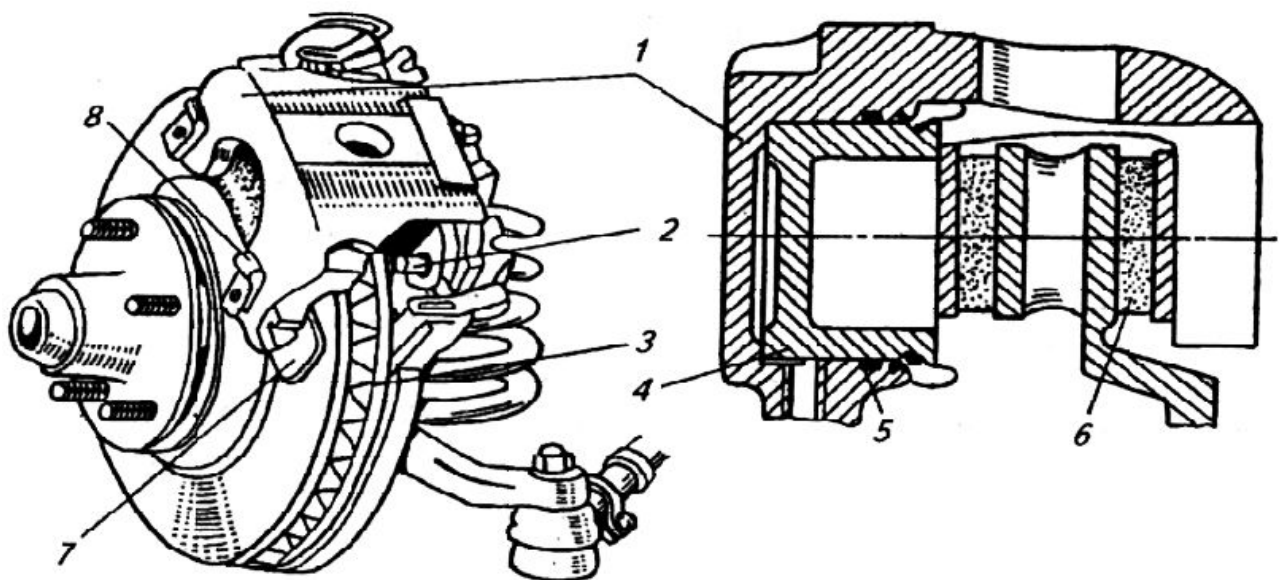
Дисковый тормозной механизм с плавающей скобой
